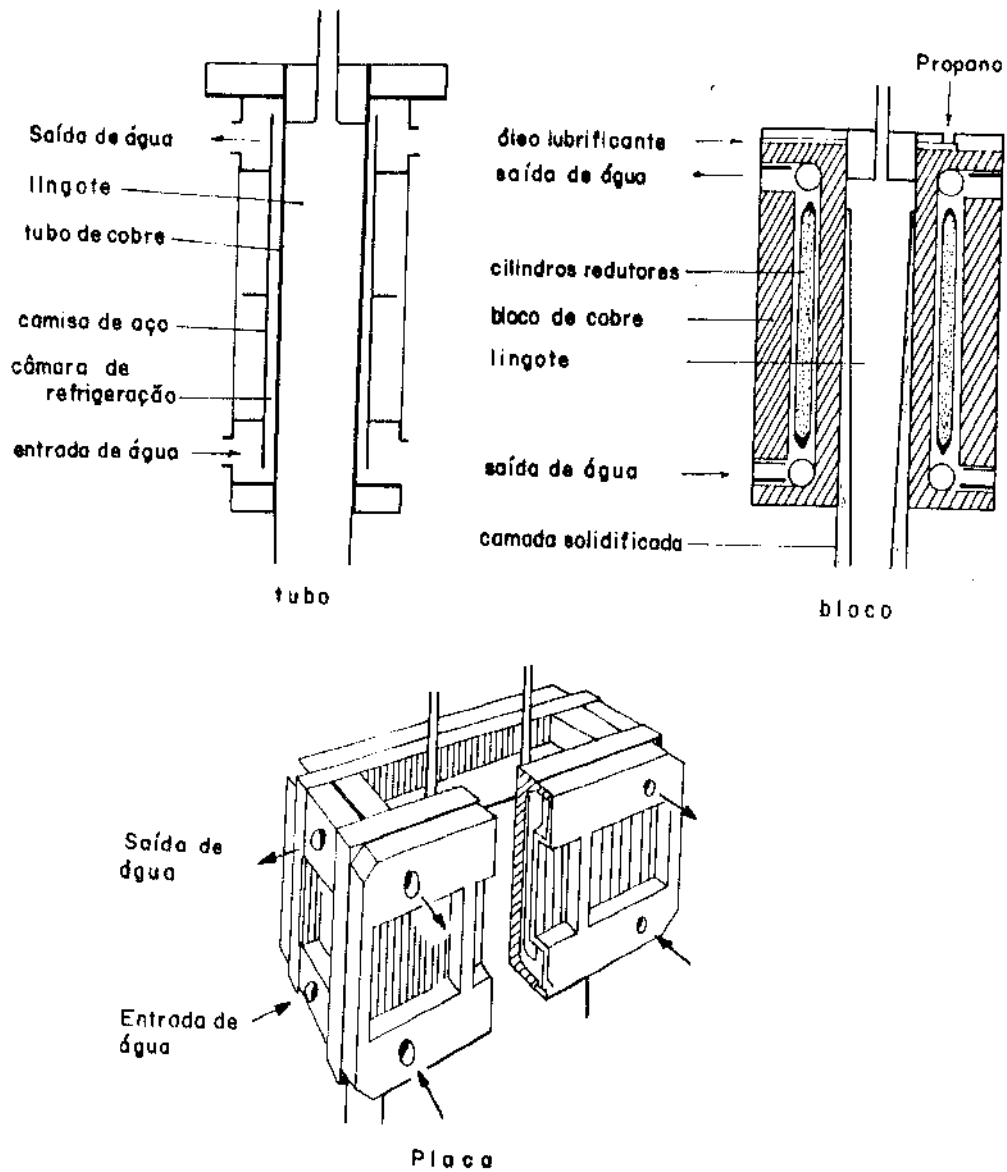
Tipos de Molde para o Lingotamento Contínuo de Aços⁽¹¹⁾
